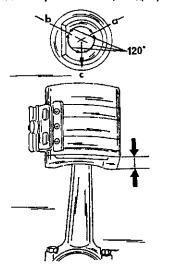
Поршень двигателя типа XU. Расположить стыки колец от "а" до "с" указанным образом. При наложении стяжной ленты поршень должен немного выступать снизу.
